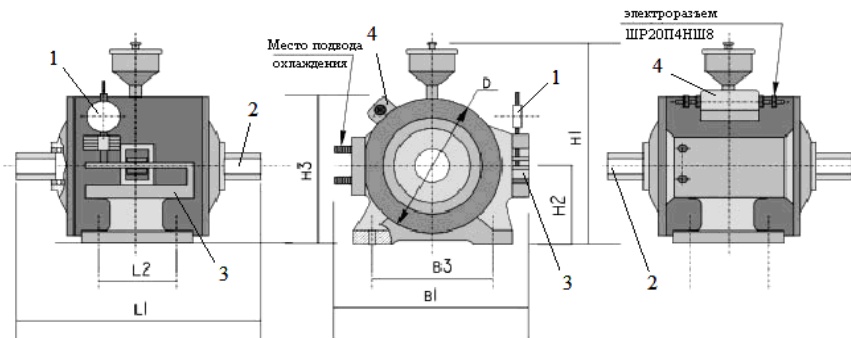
Присоединительные и габаритные размеры ПЭТ ПТ-250М:
